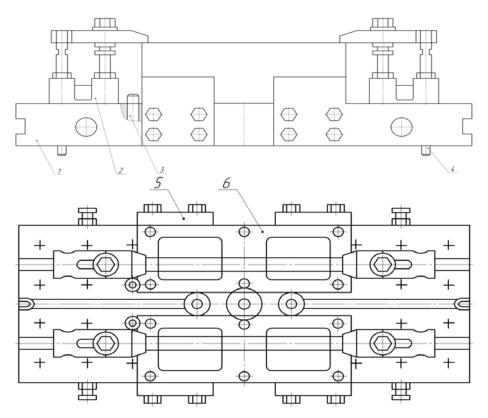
Сборно-разборное двухместное приспособление (СРП – ЧПУ) для установки корпуса: 1- плита; 2- прижим; 3, 4- базирующие пальцы; 5- планка; 6- заготовка
